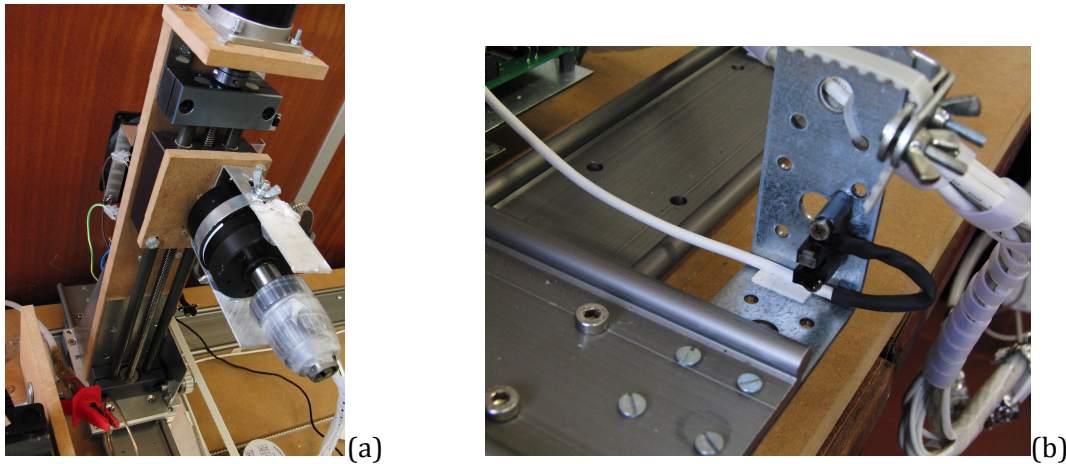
Pormenor da instalação do motor de rotação no eixo vertical (a); Pormenor da instalação do sensor óptico(b).
